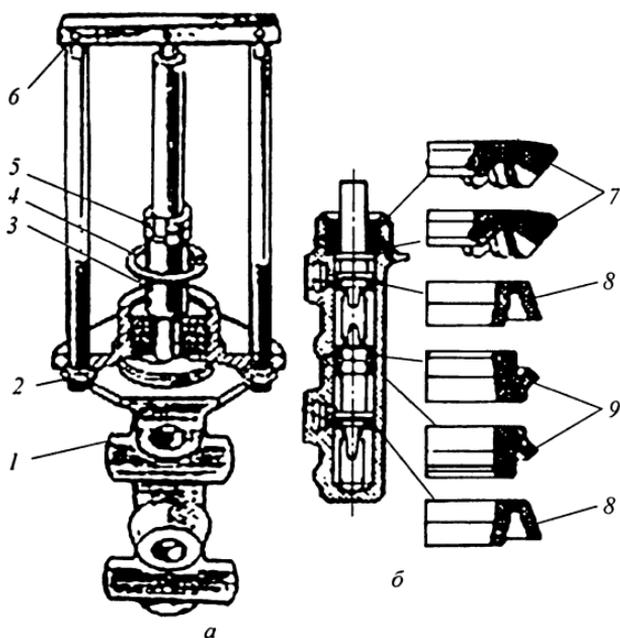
Приспособление для сборки главного тормозного цилиндра: *а* — установка главного тормозного цилиндра; *б* — расположение манжет; 1 — цилиндр; 2 — стойка; 3 — шток; 4 — запорное кольцо; 5 — полукольцо; 6 — траверса; 7, 8, 9 — манжеты
